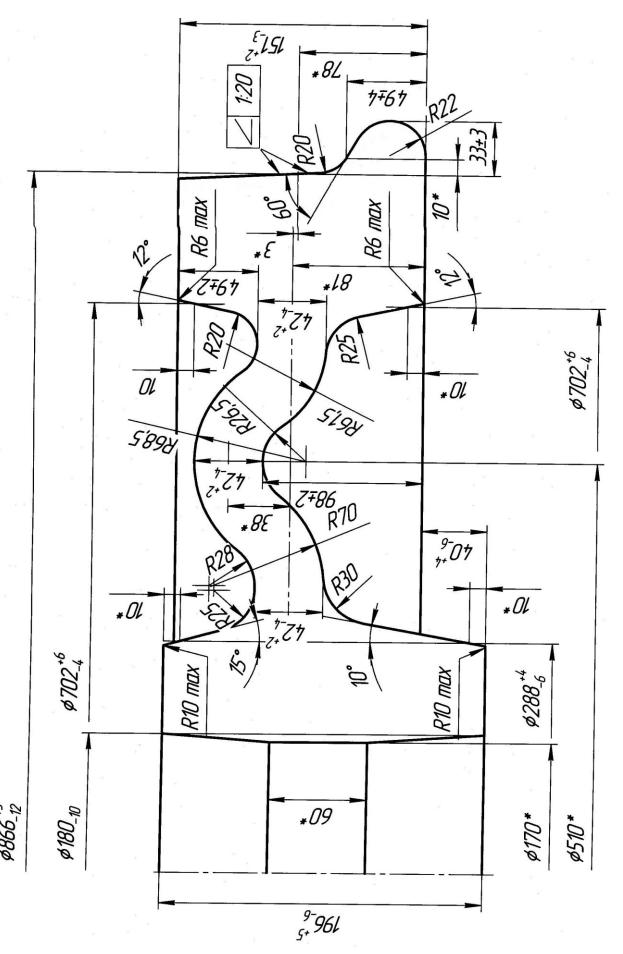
Черновое колесо Ø 866 мм (под чистовое Ø 840 мм, черт. № КР-0084-12.1). Масса чернового колеса 471 кг.
